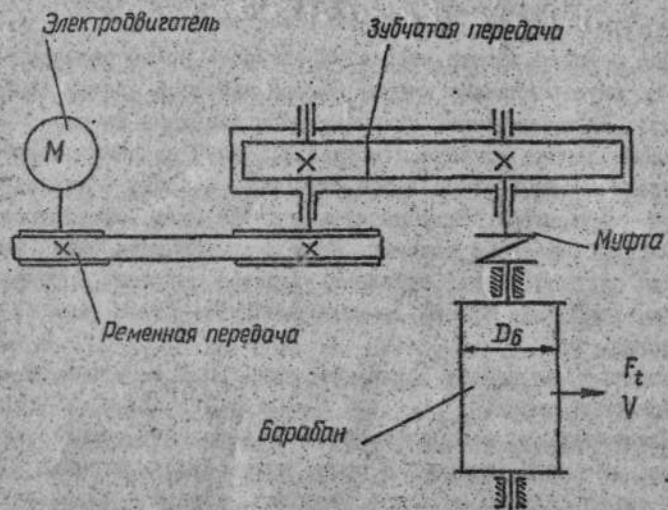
Схема привода ленточного транспортера для транспортировки багажа в аэровокзалах
